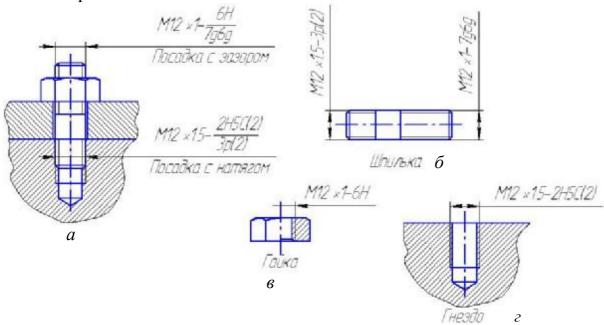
Обозначение допусков и посадок на чертежах: а — соединение деталей с наружной и внутренней резьбой; б — шпилька с резьбой; в — гайка; г - гнездо с внутренней резьбой
